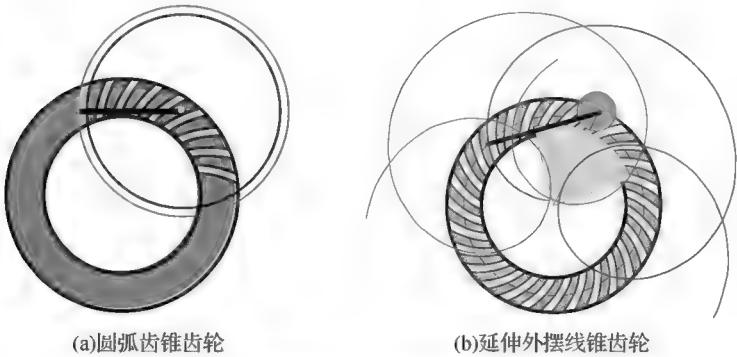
圆弧齿锥齿轮和摆线齿锥齿轮
